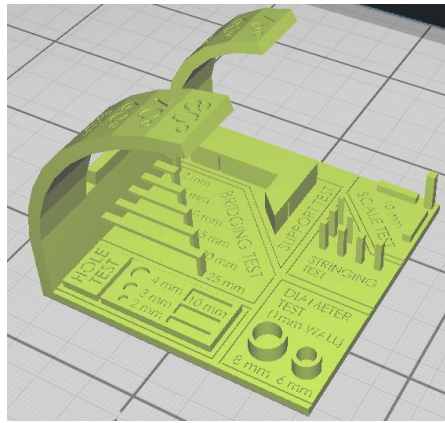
Тестова деталь в стадії підготовки до 3D-друку
